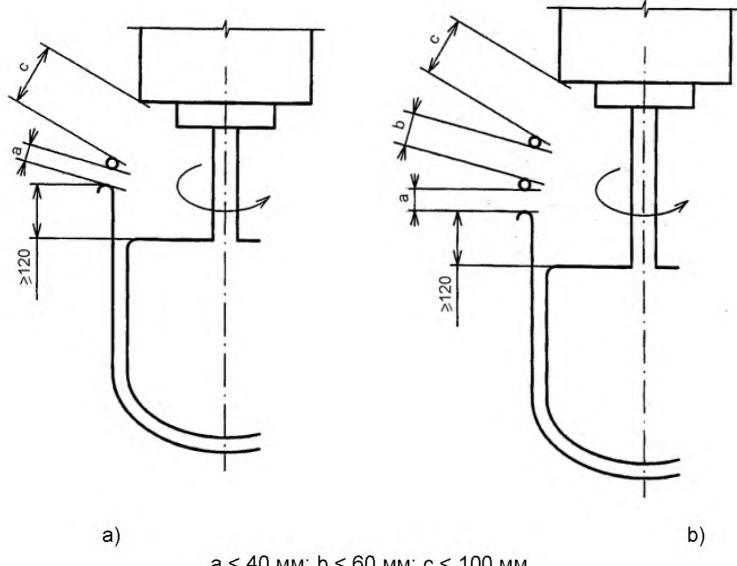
Планетарные мешалки класса 2 с защитными штангами
